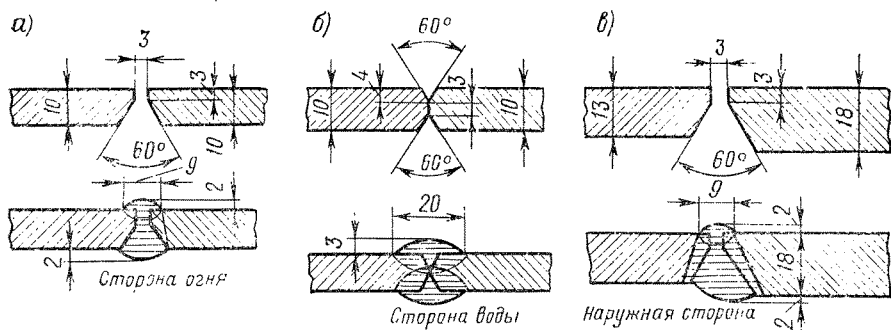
Сварные швы огневой коробки и кожуха топки:
